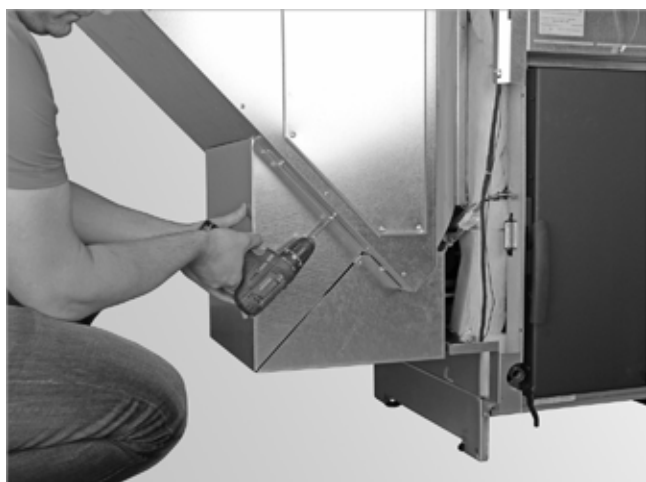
Sechs Stück Schrauben lockern, Abdeckung abnehmen
